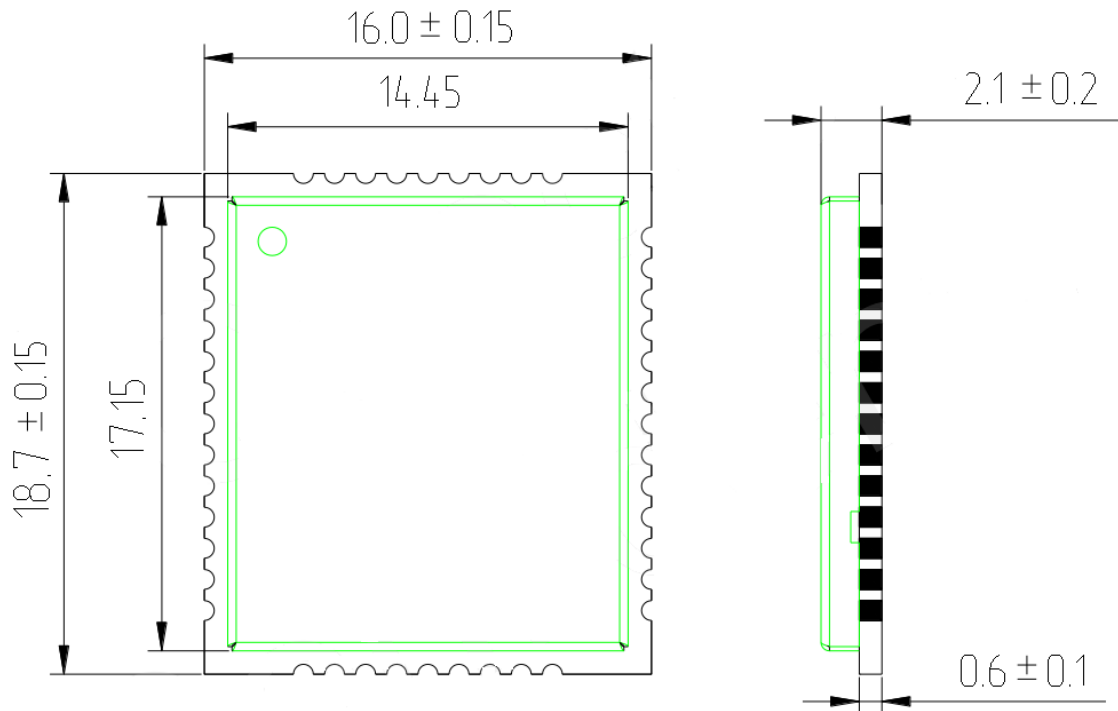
Габаритный чертеж модуля ПР503 (вид сверху и сбоку)
